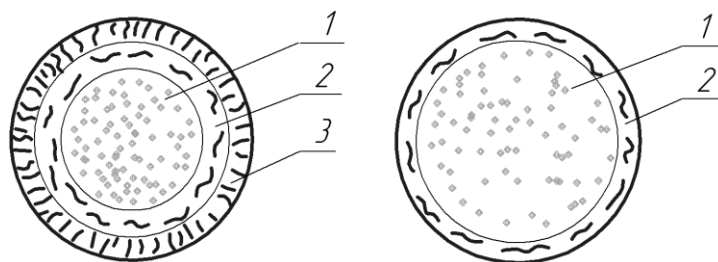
Зони деформацій на контактній поверхні зразка:
